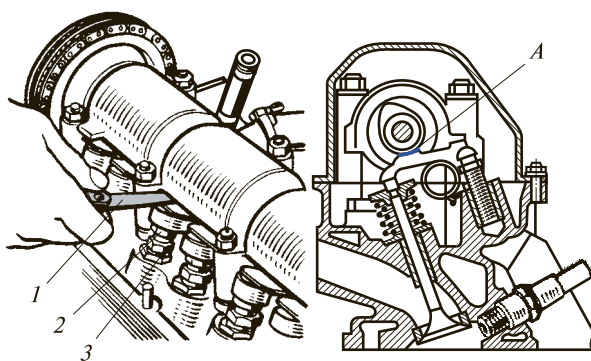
Регулировка зазора в распределительном механизме двигателя ВАЗ-2101, -2103, -2105, -2106:
